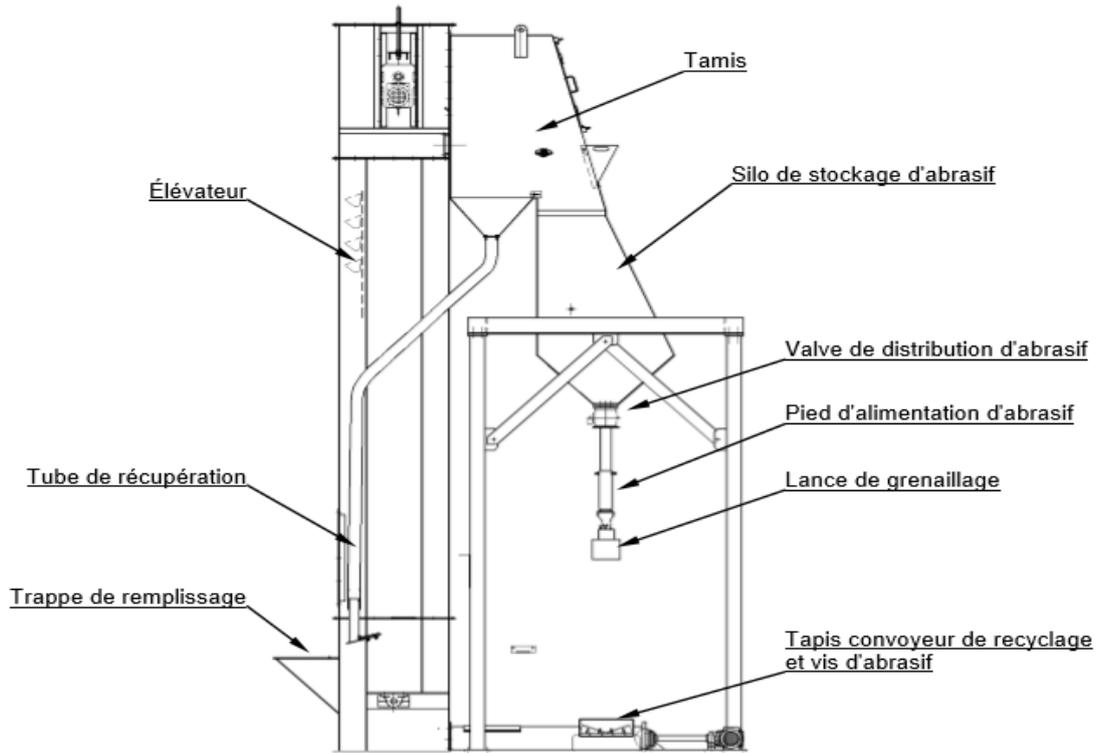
Vue de face de l'unité de grenailage intérieur [2]
